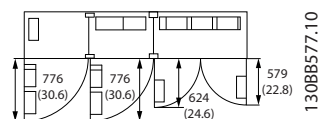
Пространство перед корпусом типа IP21/IP54, типоразмер F13
